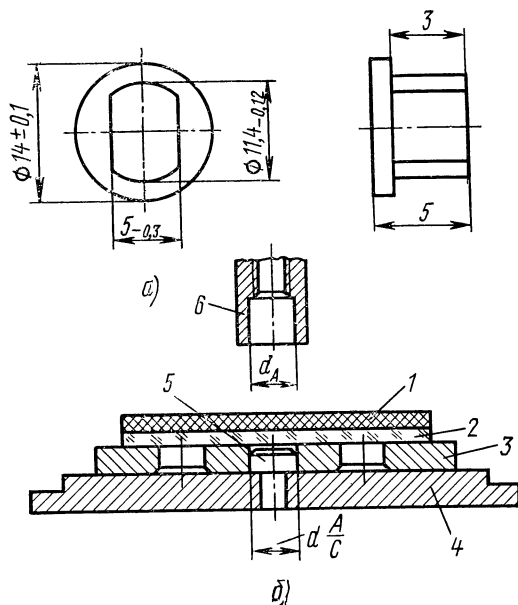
Корпус (а) из стекла и приспособление (б) для ориентирования заготовок при его изготовлении:
